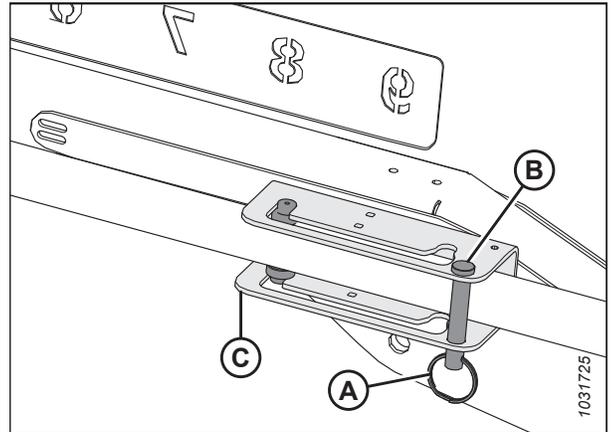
Cilindro del braccio sinistro – Posizione avanzata
